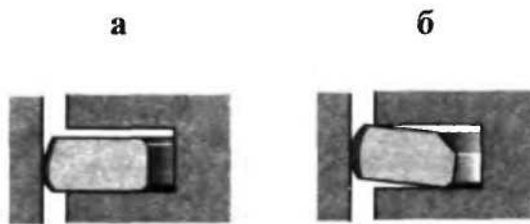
Технічні рішення одержання несиметричної бочкоподібною поверхні кілець: а - спеціальною обробкою зовнішньої поверхні; б - закручуванням кільця при його роботі завдяки виготовленню фаски на внутрішній поверхні кільця.
